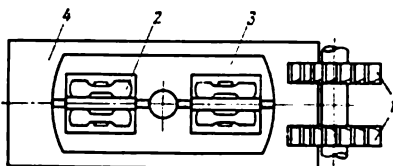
Schéma d'exécution des faces des leviers sur une fraiseuse horizontale à plateau d'indexage:
